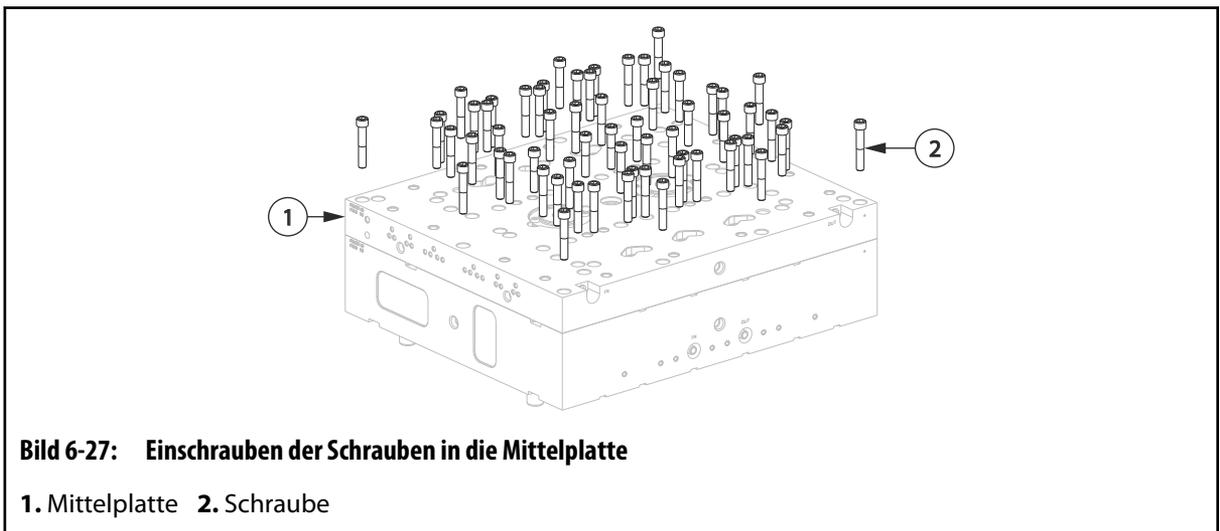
Einschrauben der Schrauben in die Mittelplatte
